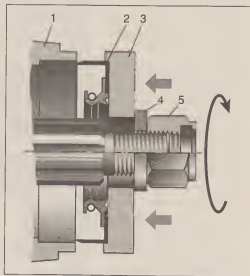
Запрессовка нового сальника: 1 — корпус; 2 — сальник; 3 — оправка; 4 — шайба; 5 — гайка.
